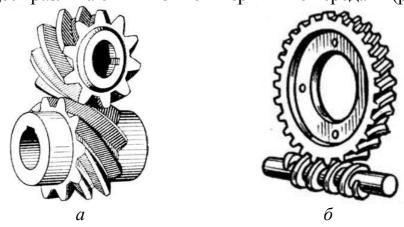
Зубчато-винтовые передачи: a — винтовая зубчатая передача; δ — червячная зубчатая передача
